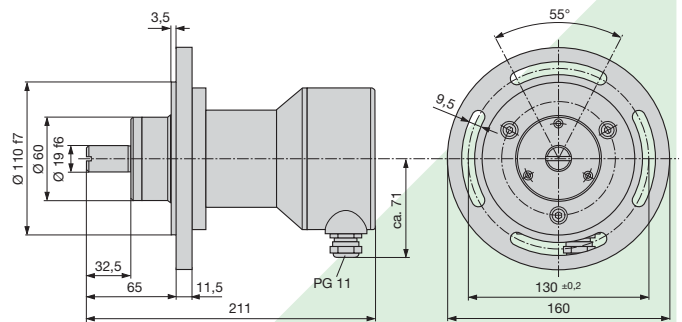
KINAX WT 717 mit Zusatzgetriebe und Flansch.
